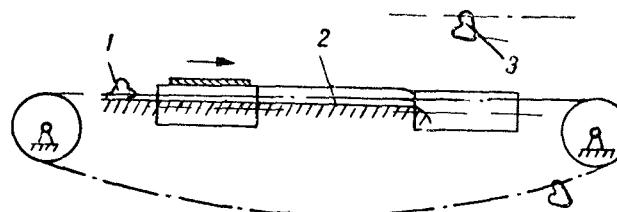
Схема цепного шлепперного транспортера с падающими захватами.
